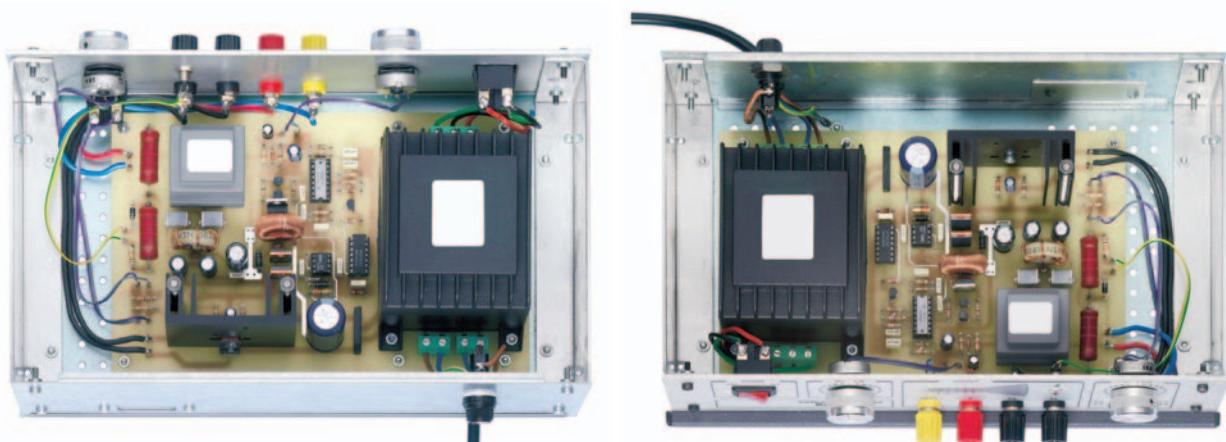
Photo d'un des prototypes de la platine du régénérateur de tube cathodique EN1659 installée dans son boîtier, vue de l'arrière (en haut) et vue de l'avant (en bas). Ces photos montrent quels éléments monter en face avant et sur le panneau arrière ; elles montrent aussi comment réaliser les interconnexions entre la platine et les deux panneaux.
